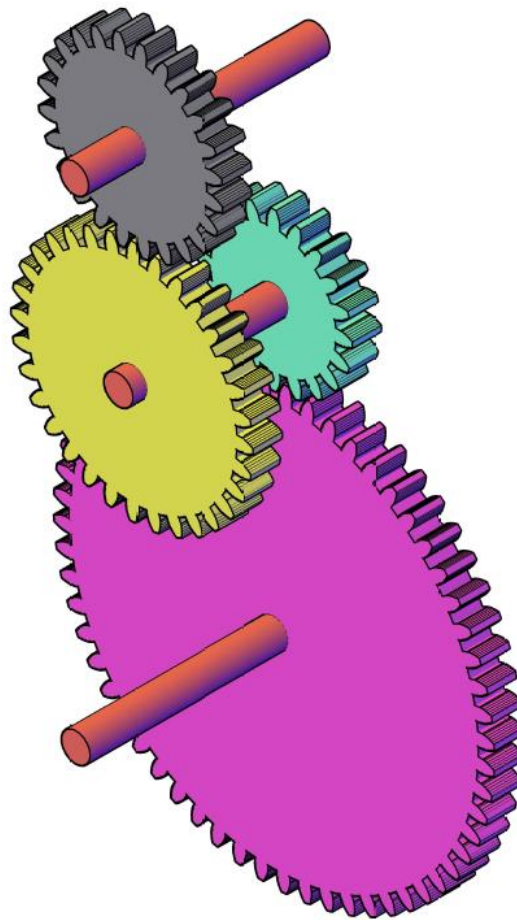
Ilustração do conjunto de engrenagens dimensionado para a caixa de redução. Fonte: Elaborada pelo autor
